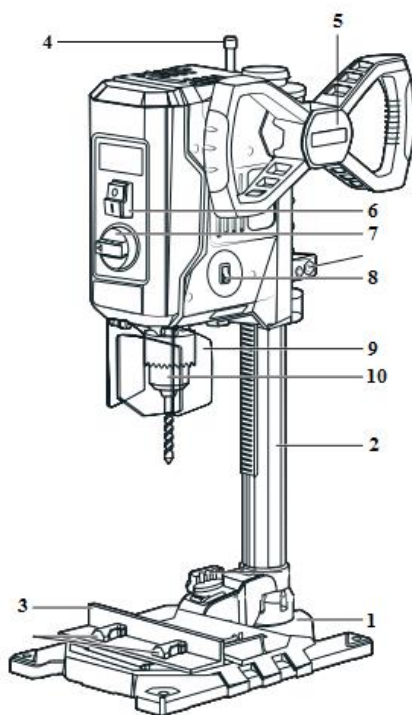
Сверлильный станок ЗУБР ВСС-П750
